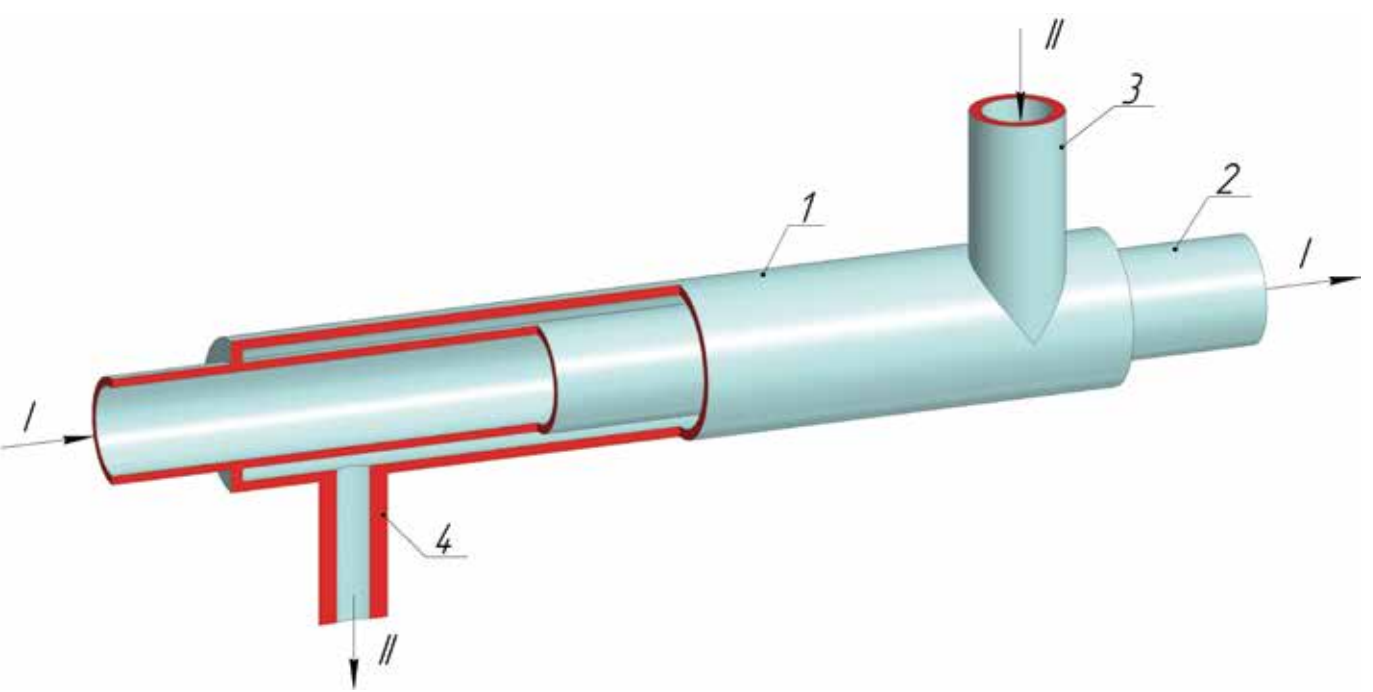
Двухтрубный теплообменный аппарат с тангенциальным расположением патрубков межтрубного пространства:
